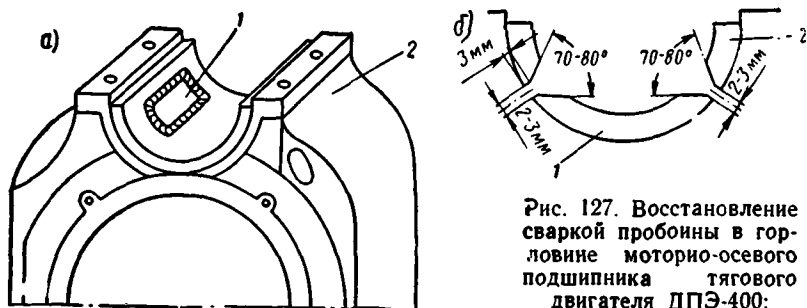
Восстановление сваркой пробойны в горловине моторно-осевого подшипника тягового двигателя ДПЭ-400:
